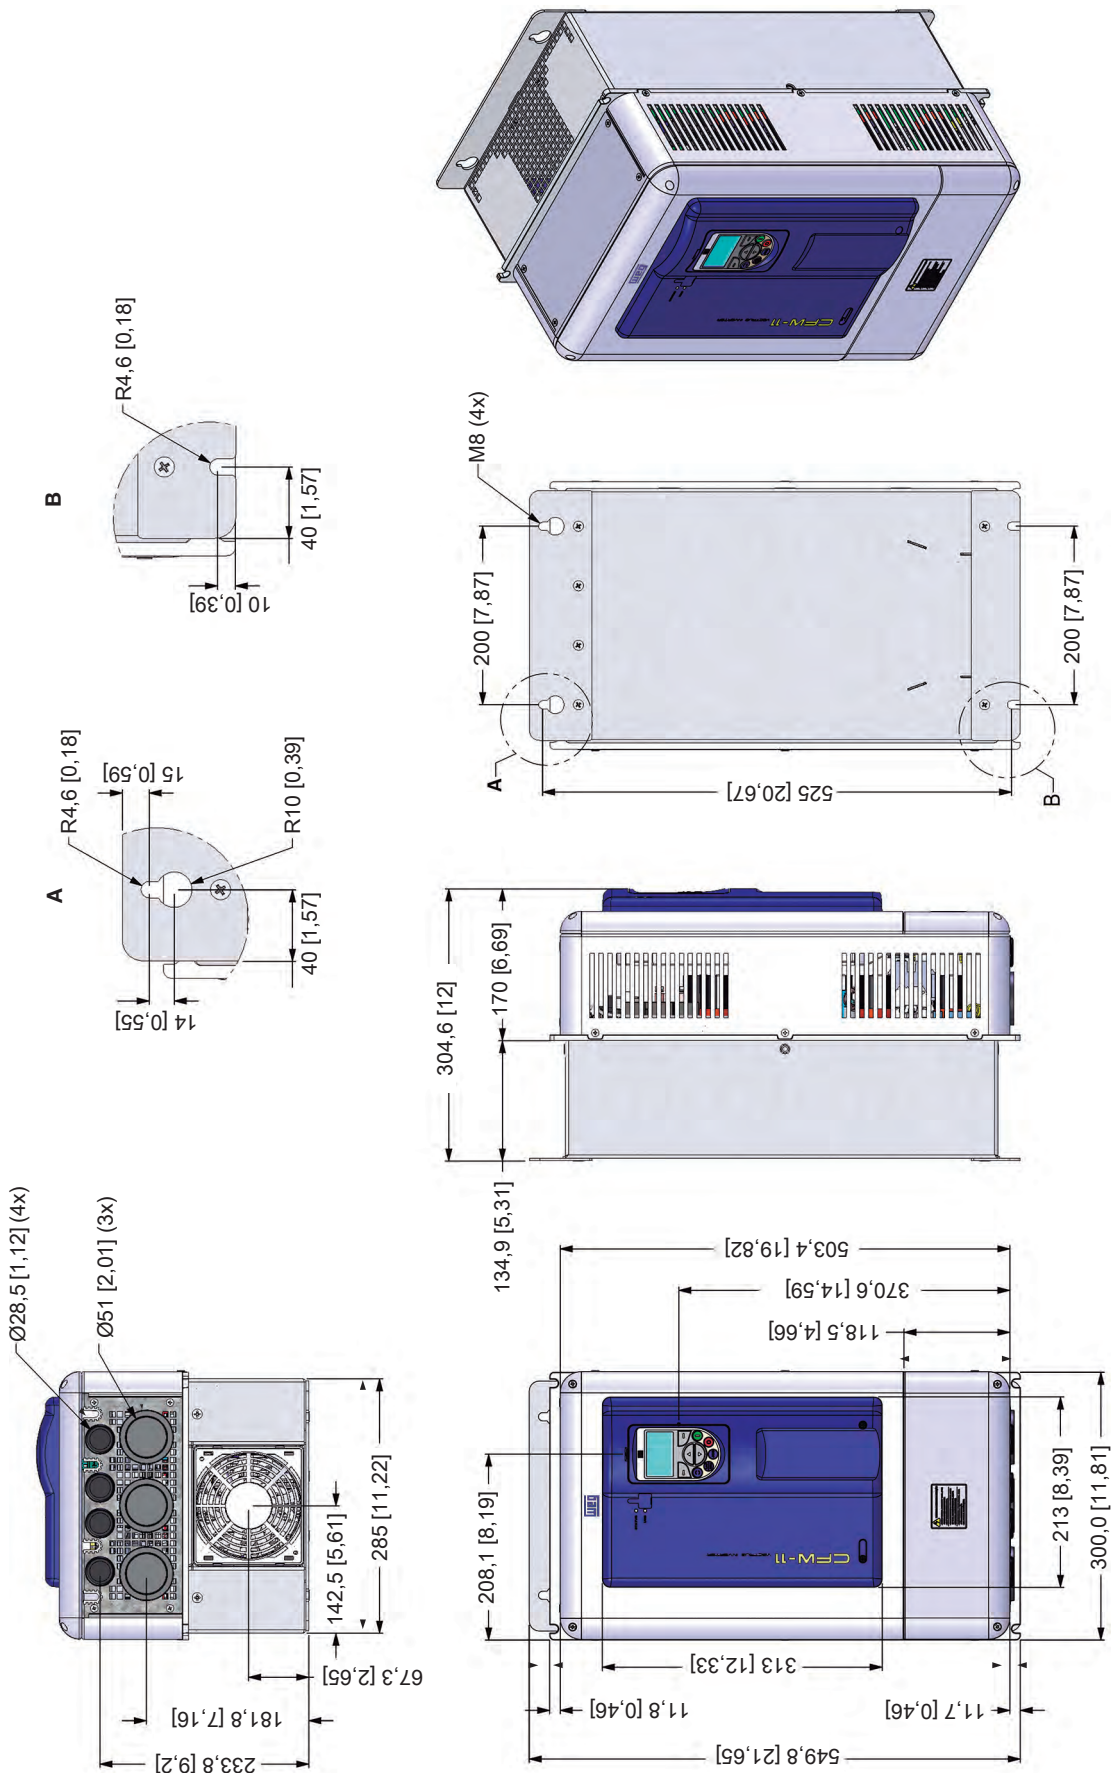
Габаритные размеры преобразователя, размер корпуса D, мм [дюйм.]
